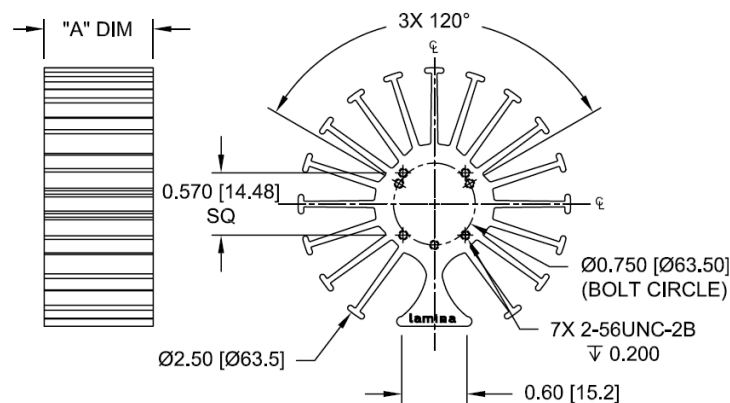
Dimensiones físicas del disipador de calor HS-4150-0345
